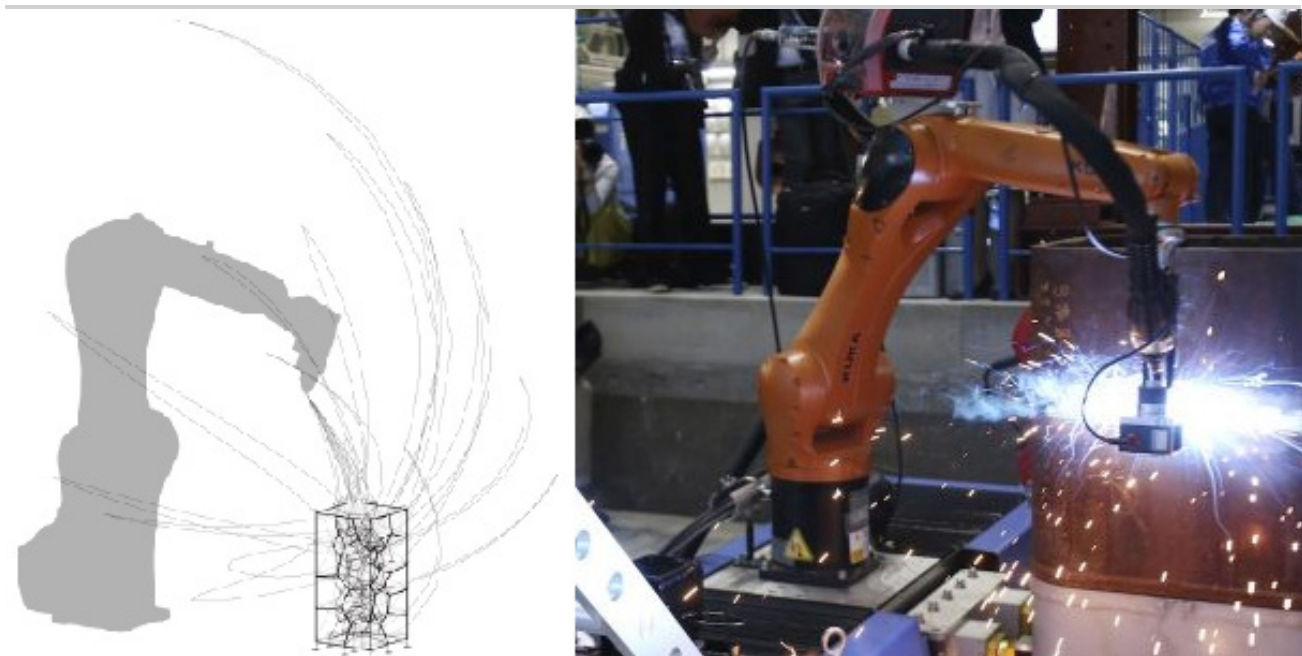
Planificación de rutas (izq.). Robot soldador autónomo de SHIMIZU (der.)
